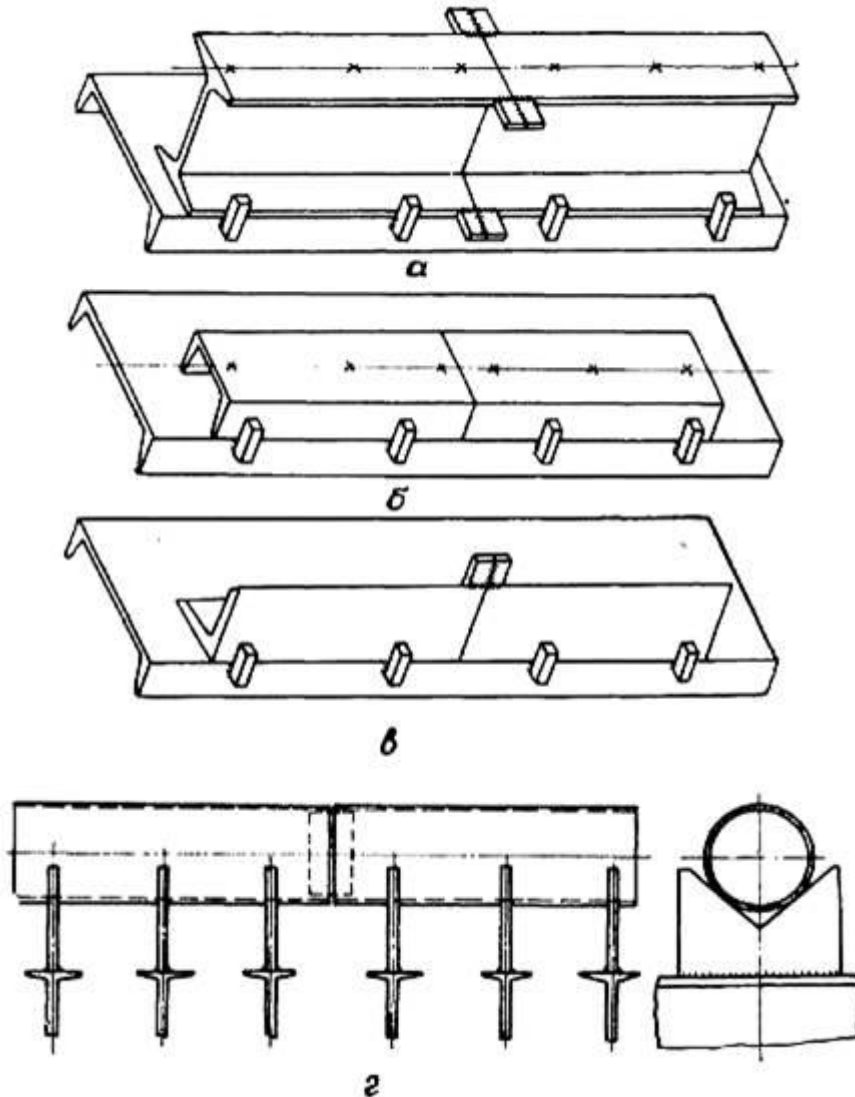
Сборка стыковых соединений сортового металлопроката и труб: а - сборка двутавровых балок; б - сборка швеллеров; в - сборка уголков; г - сборка труб.
